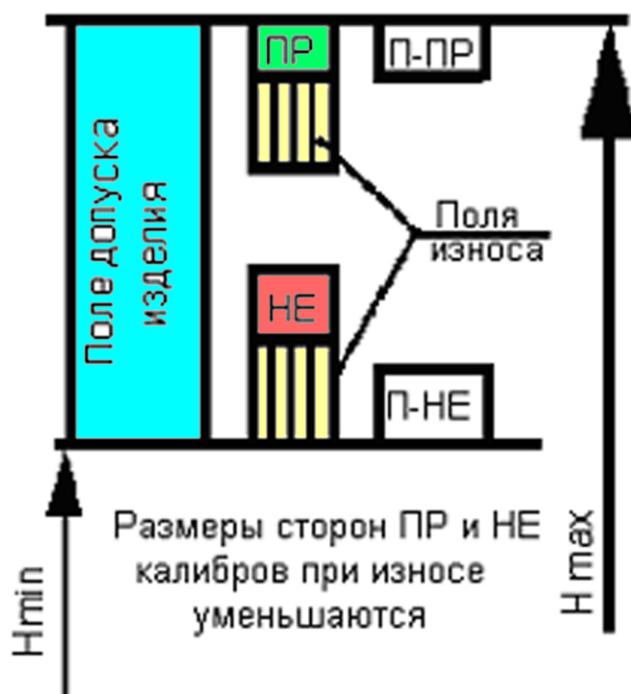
Поля допусков калибра для контроля высот уступов (схема 1).
